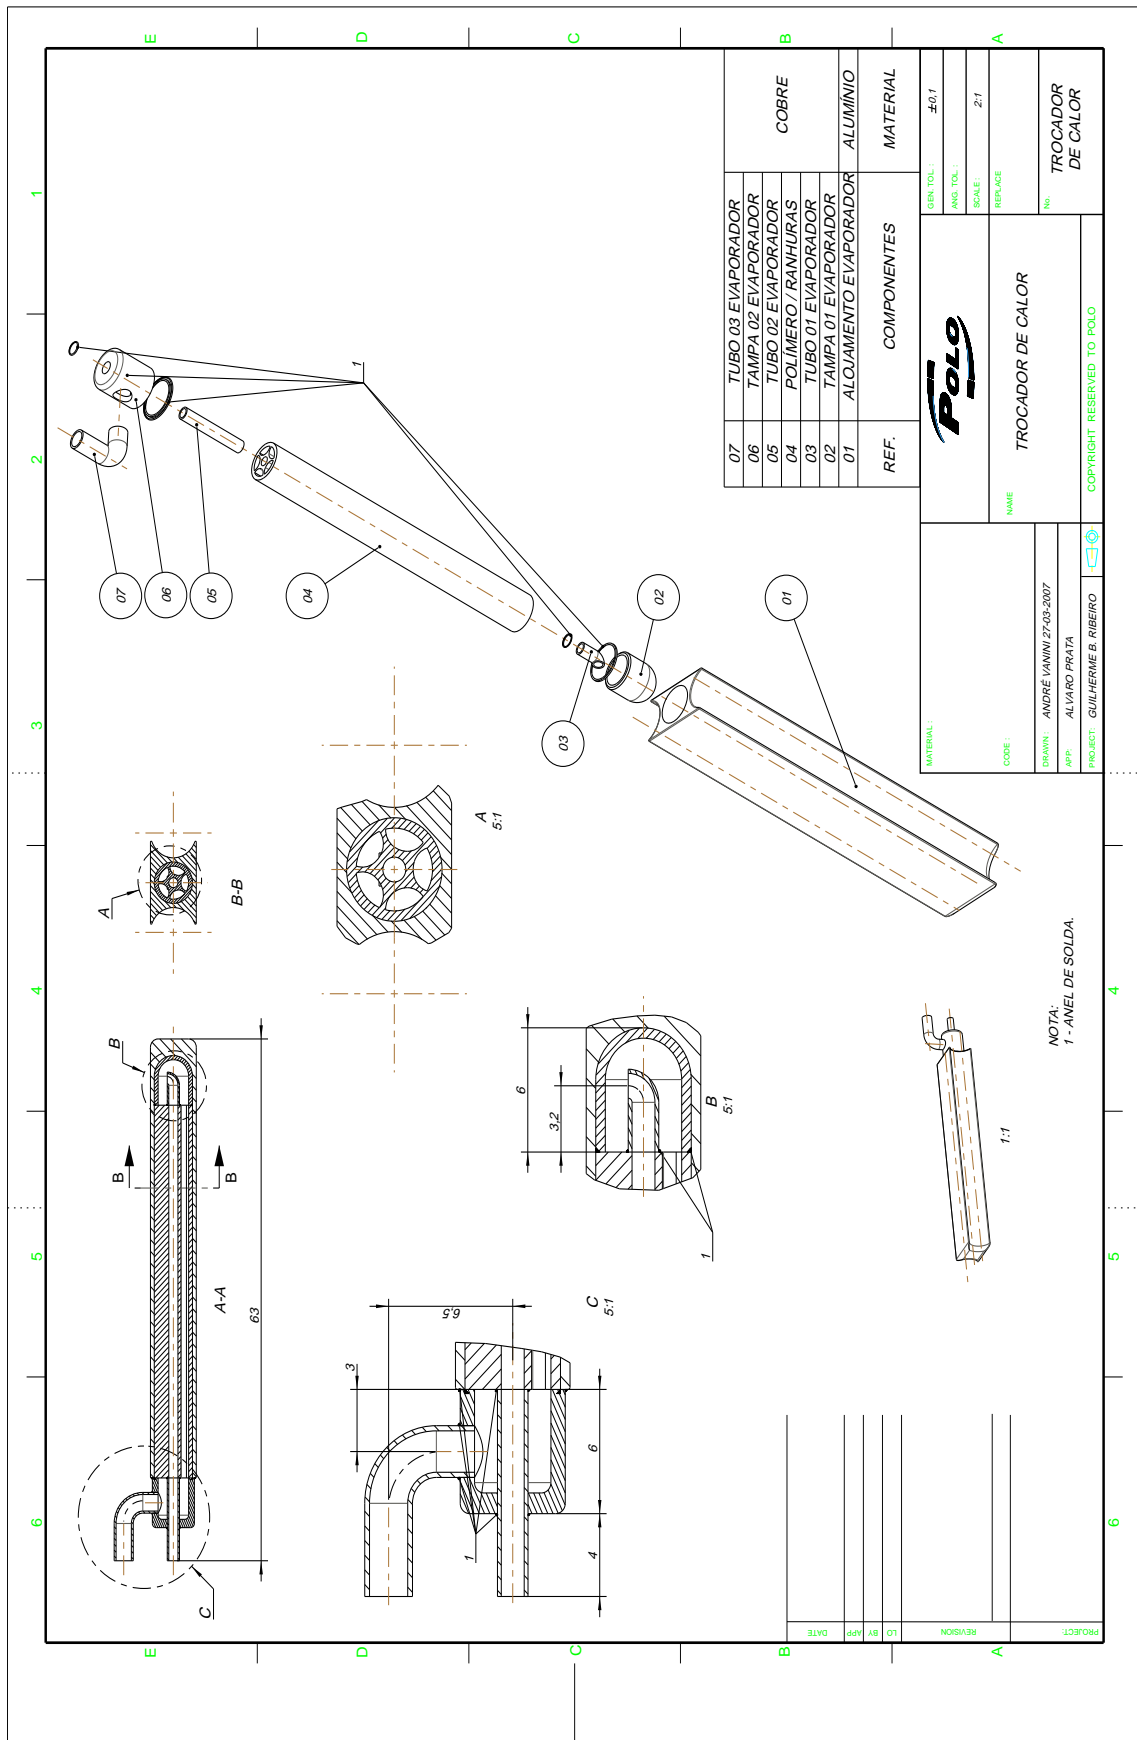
Desenho técnico do evaporador acoplado a tubos de calor - Parte I.
